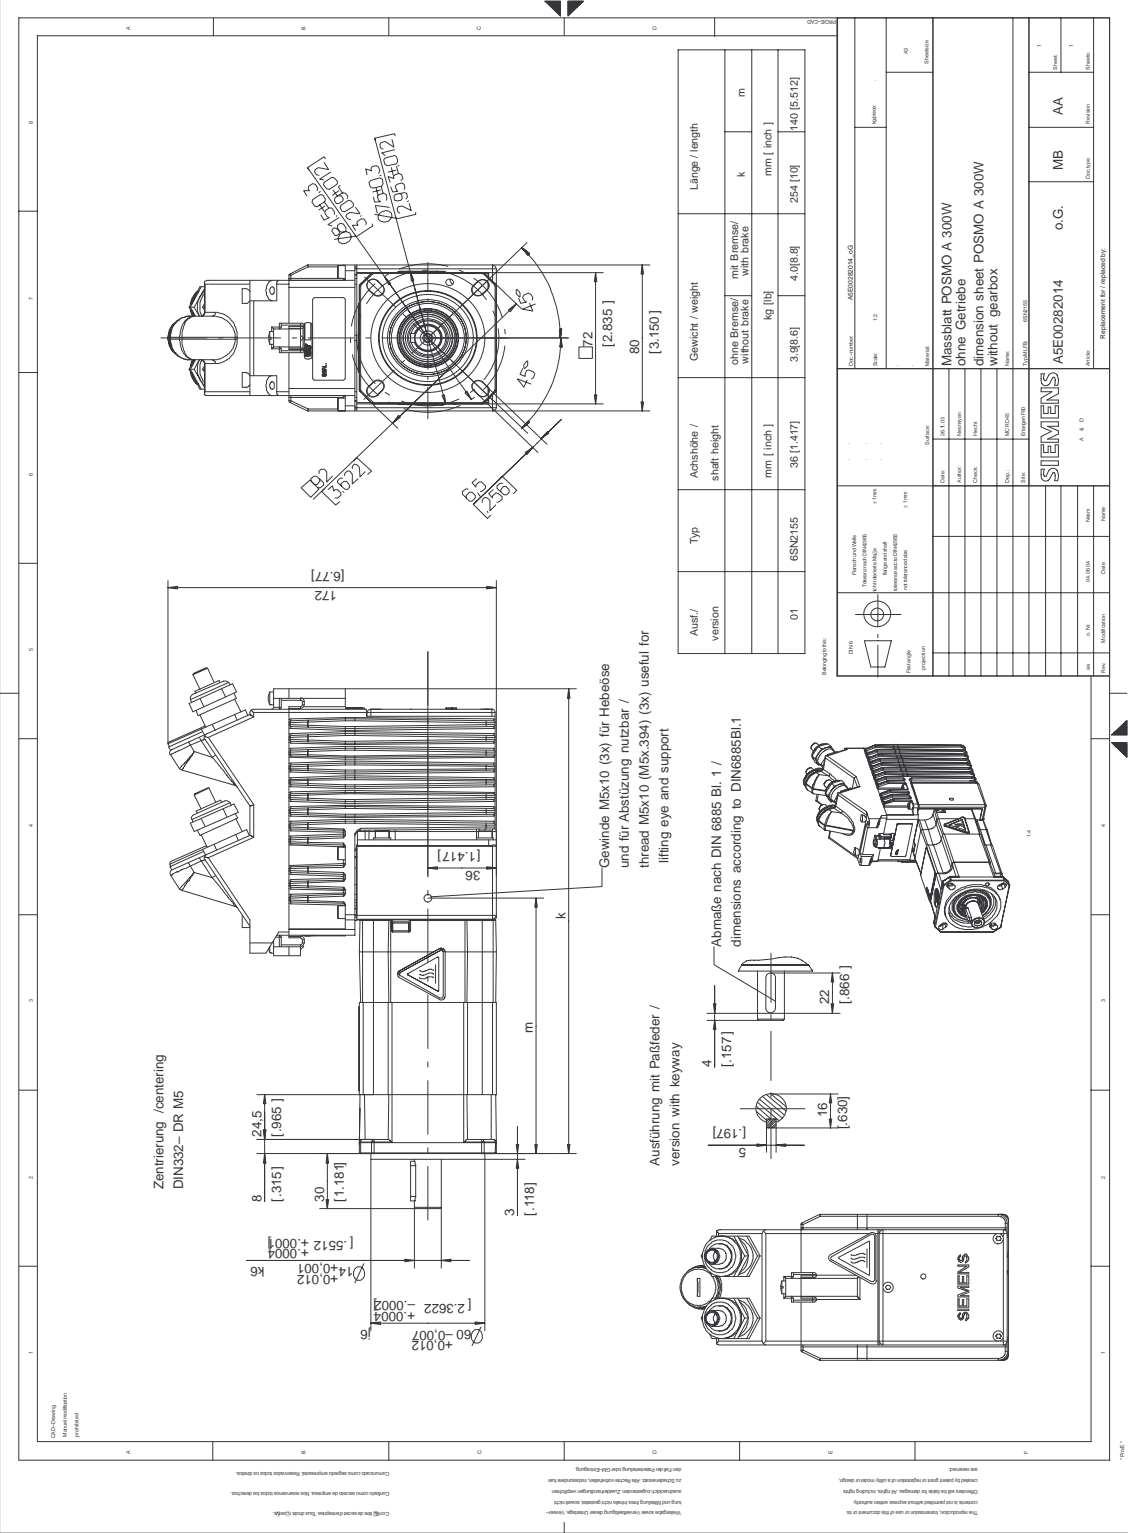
Maßblatt: SIMODRIVE POSMO A – 300 W ohne Getriebe
